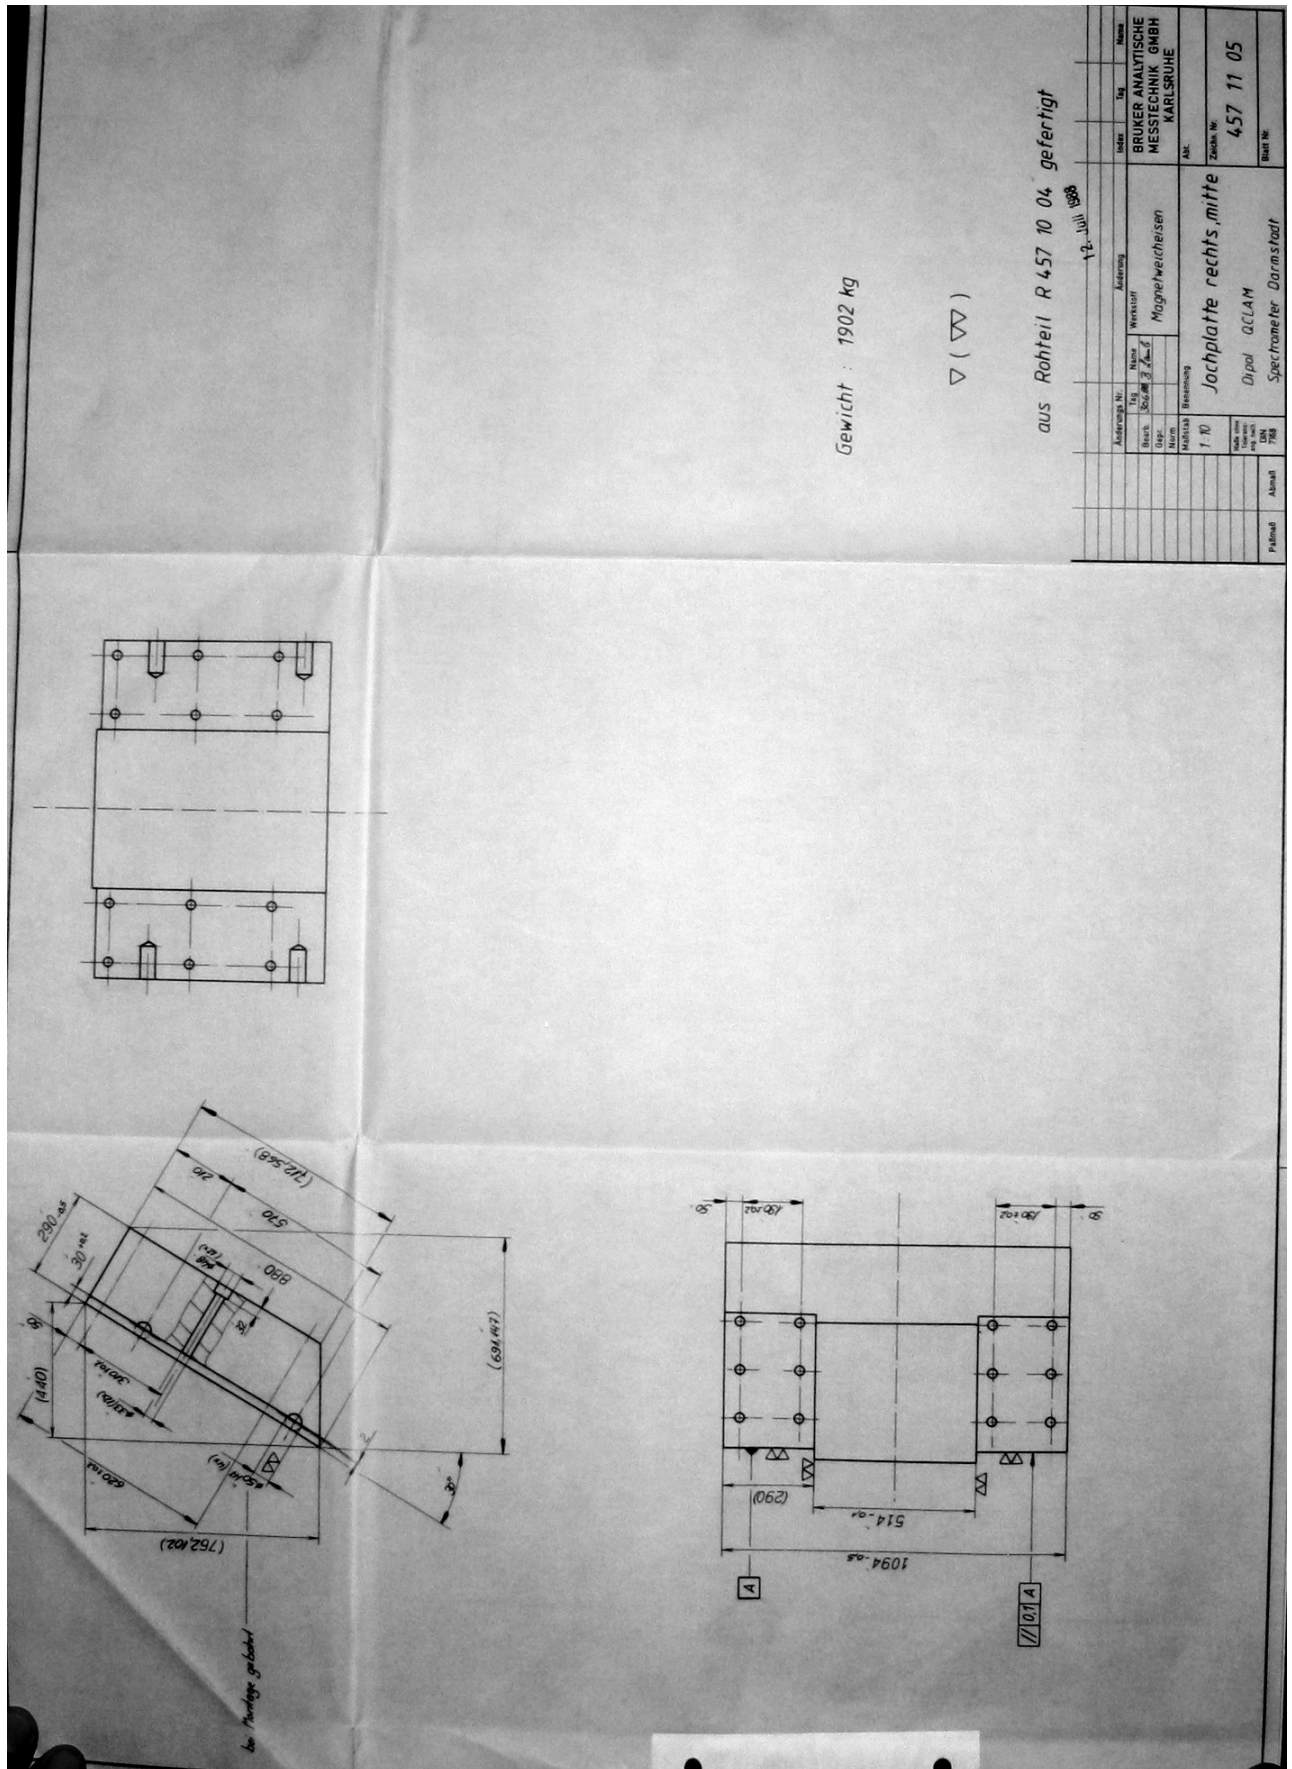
Technische Zeichnung der rechten mittleren Jochplatte des QClams.
